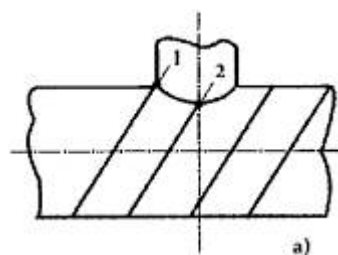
а. Сварка патрубков (штуцеров) с трубопроводами со спиральными швами: спиральный шов не допускается;
